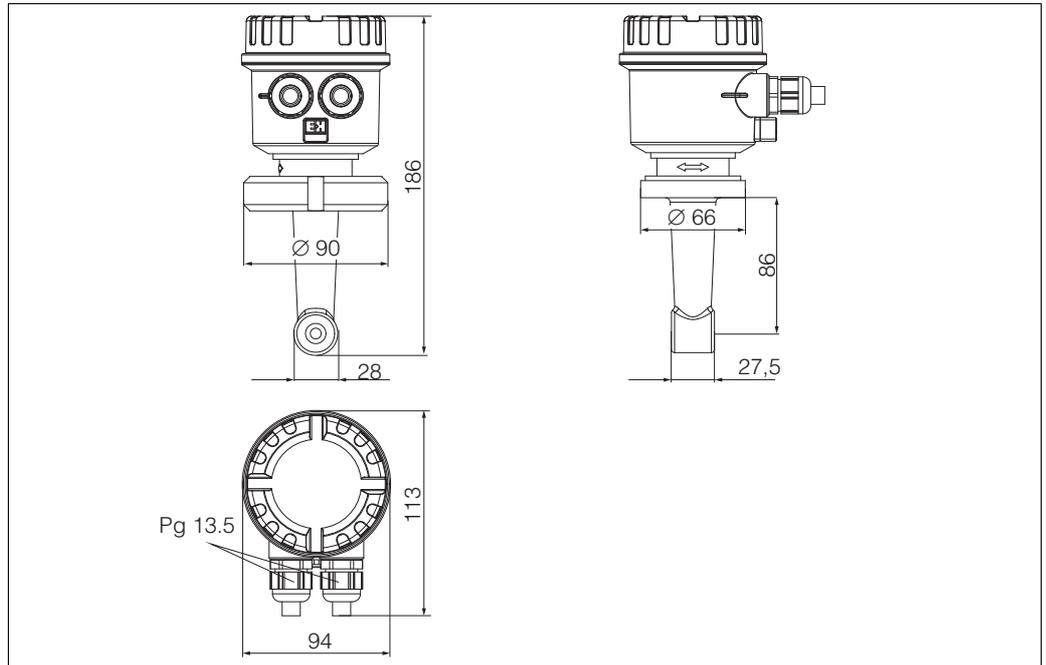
Dimensions CLD133 ; gauche : avec écrou-raccord ; droite : sans écrou-raccord
